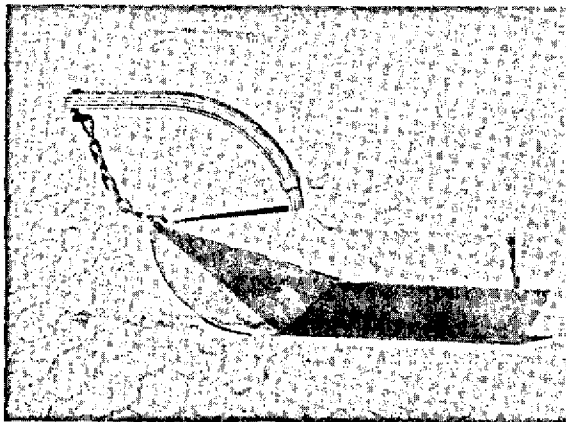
Sulcador construído com chapas soldadas.
